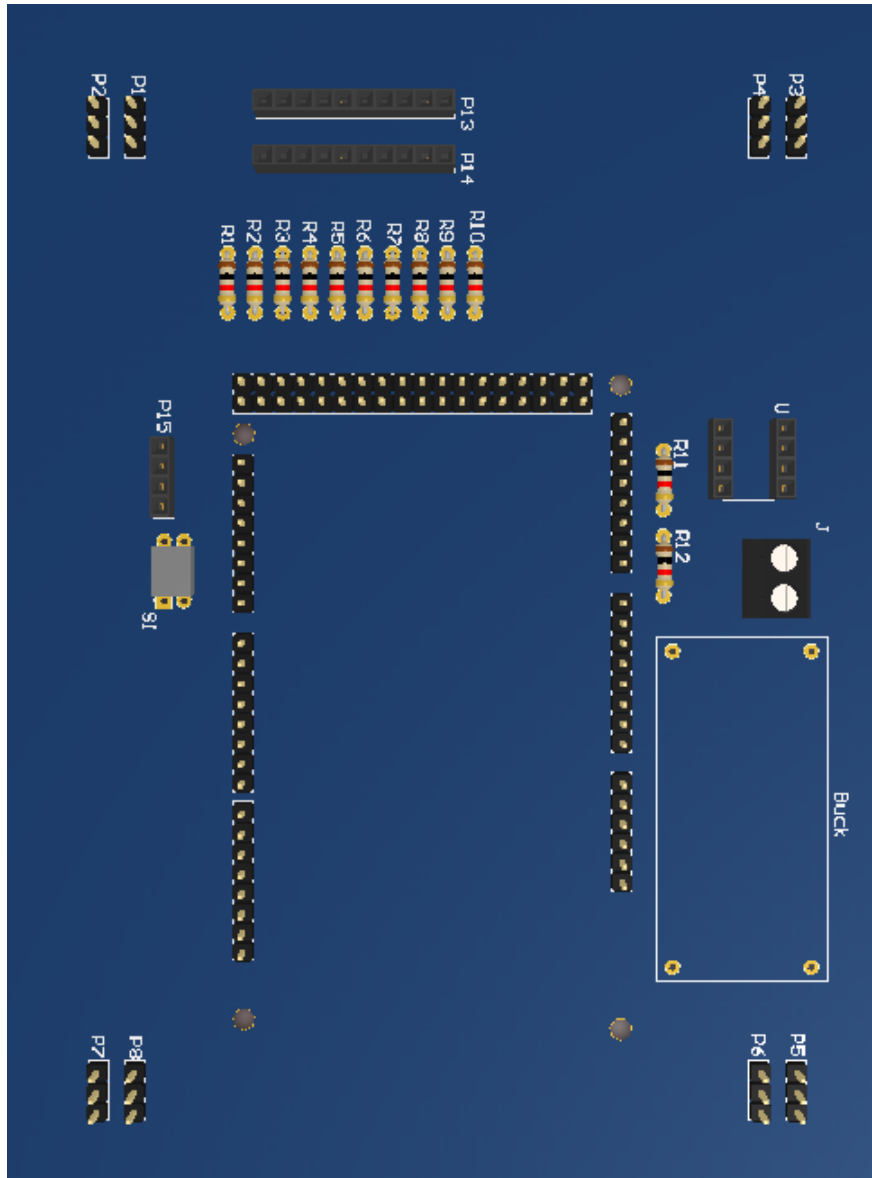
Vista 3D del PCB creado para interconectar los componentes del robot
